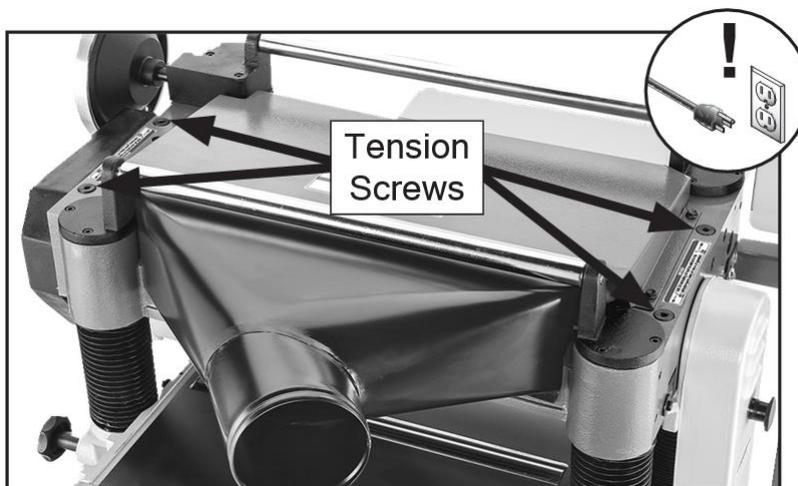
Расположение винтов регулировки натяжения роликовой пружины.
